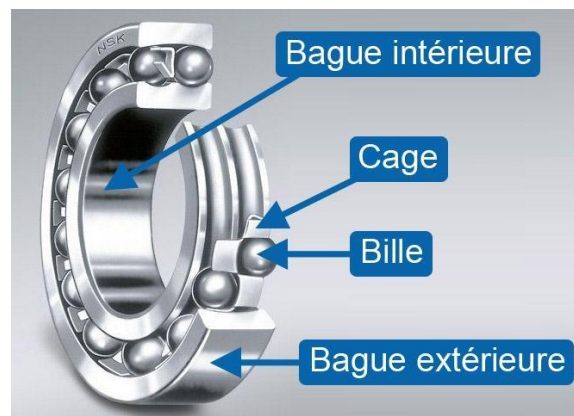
Vue éclatée des éléments constitutifs d'un roulement billes .
